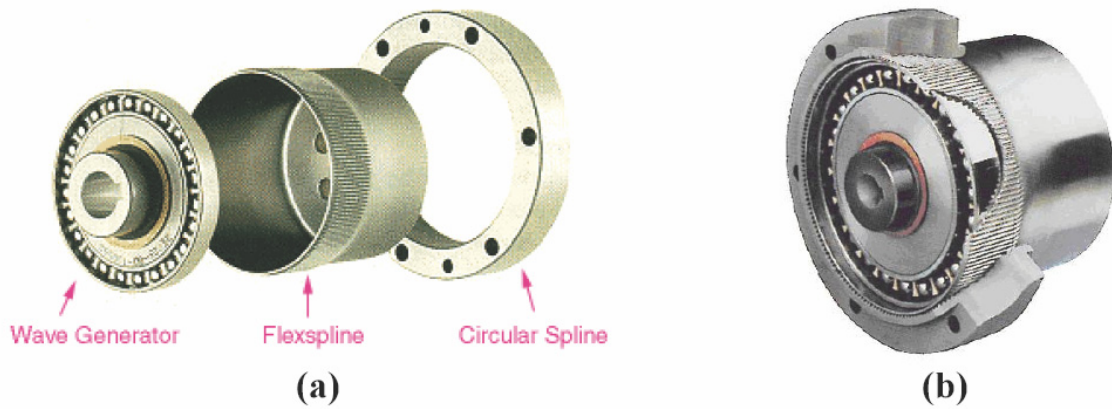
(a) Despiece del HD (b) Ensamblaje de HD típico [3].
